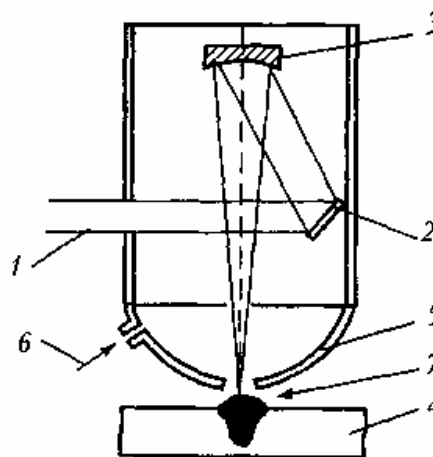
Схема лазерной сварки: 1 – луч лазера; 2 – отражающее зеркало; 3 – фокусирующее зеркало; 4 – заготовка; 5 – сегментная перегородка; 6 – защитный газ; 7 – плазмоподавляющий газ
